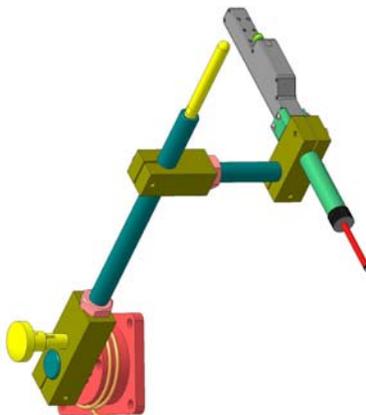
Общий вид измерительного приспособления с базированием на кожухе шлифовального круга
